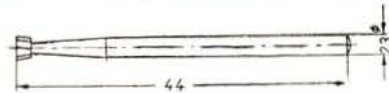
Bohrer, lange Form (Maßstab 1 : 1)
